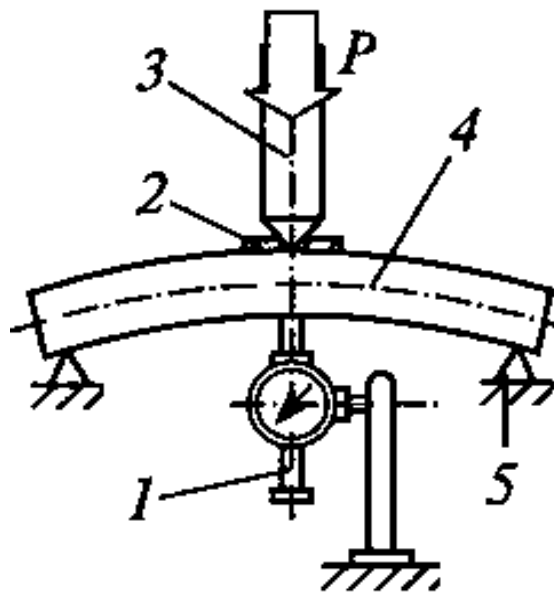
Схемы плавки вала прессом: 1 — индикатор; 2 — прокладка; 3 — нажимной шток; 4 — вал; 5 — опоры
